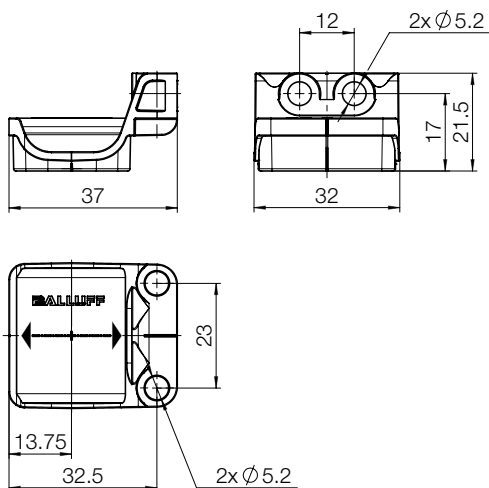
Misure di montaggio trasduttore di posizione BAM TG-IR-036-A, la freccia indica la direzione di movimento (per il montaggio vedere Fig. 5-3)
